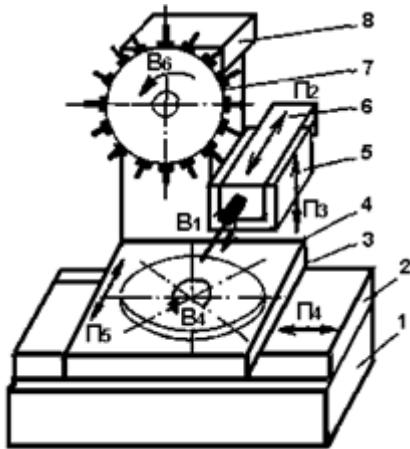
Схема компоновки багатоопераційного верстата з горизонтальним шпинделем
